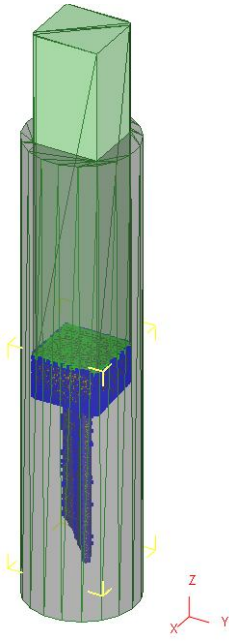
Модель робочої порожнини штампу в DEFORM-3D
